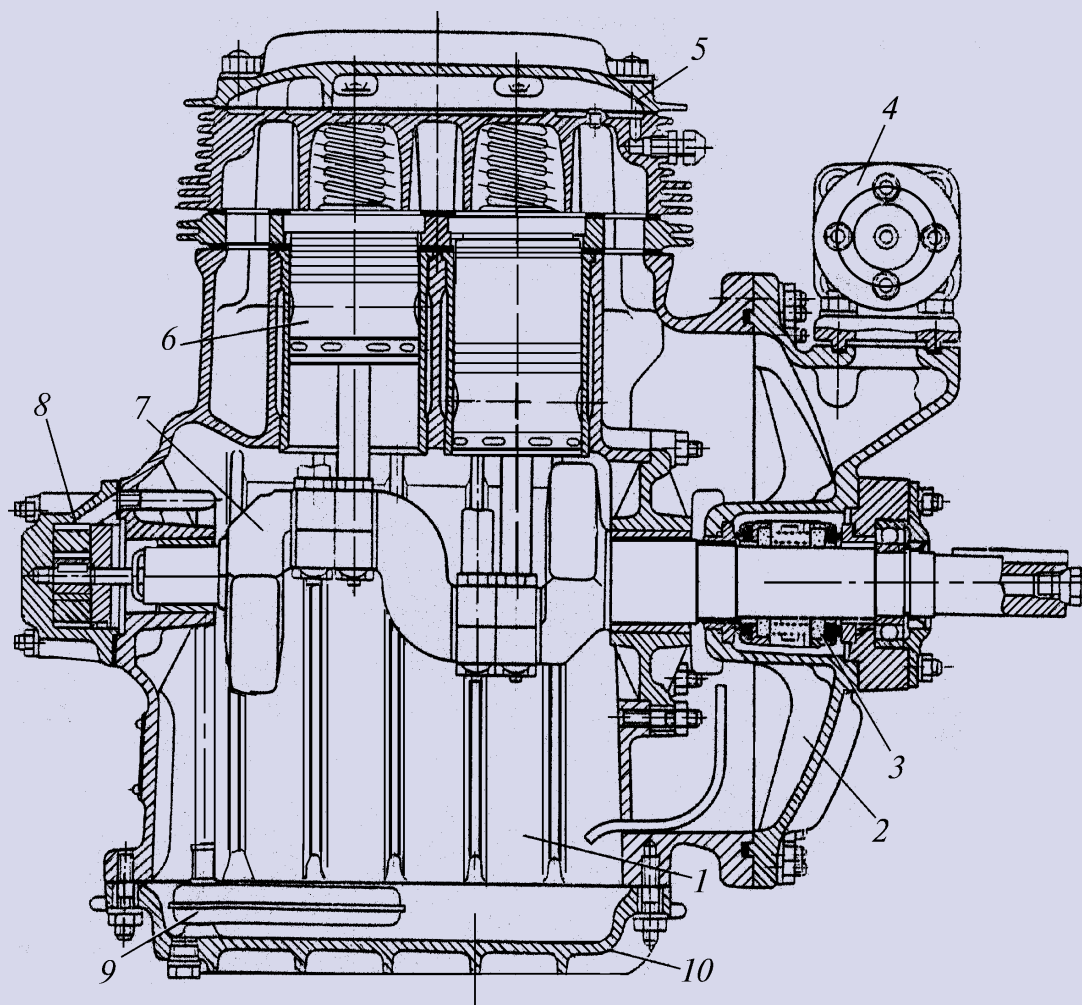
Компрессор типа «V» установки МАВ — II: 1 — корпус; 2 — крышка корпуса; 3 — сальник; 4 — всасывающий вентиль; 5 — головка цилиндров; 6 — шатунно-поршневая группа; 7 — коленчатый вал; 8 — масляный насос; 9 — масляный фильтр; 10 — поддон
